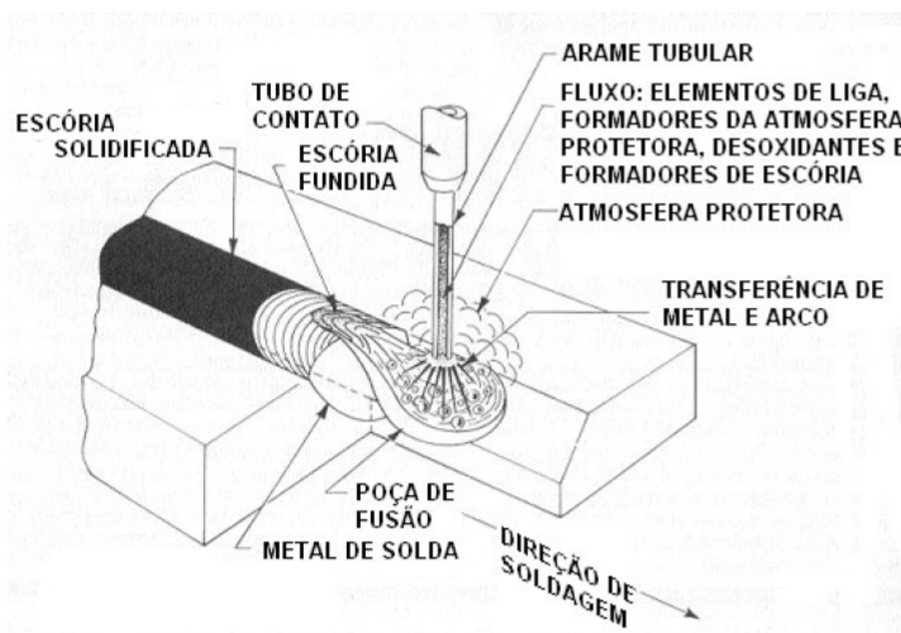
Soldagem com arame tubular autoprotegido (FORTES, 2004)
